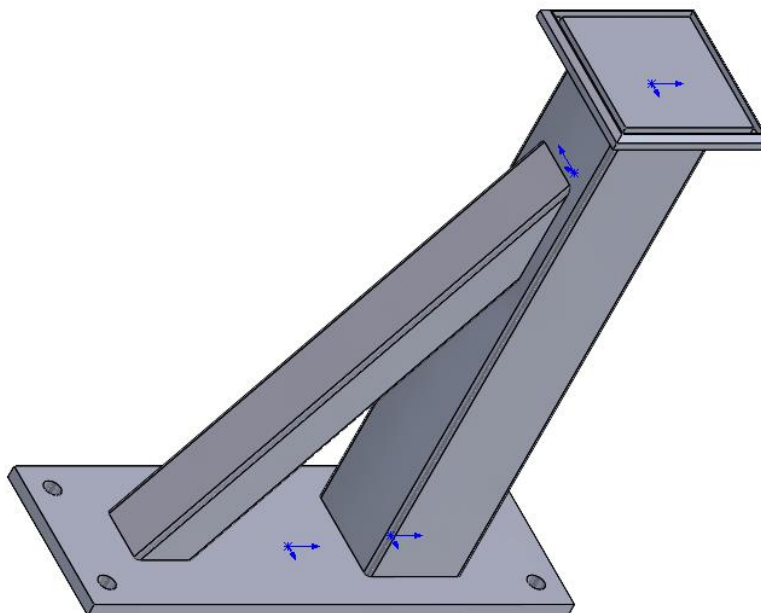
Подставка 1 (4А.0001.000 СБ) в сборе, изометрический вид
